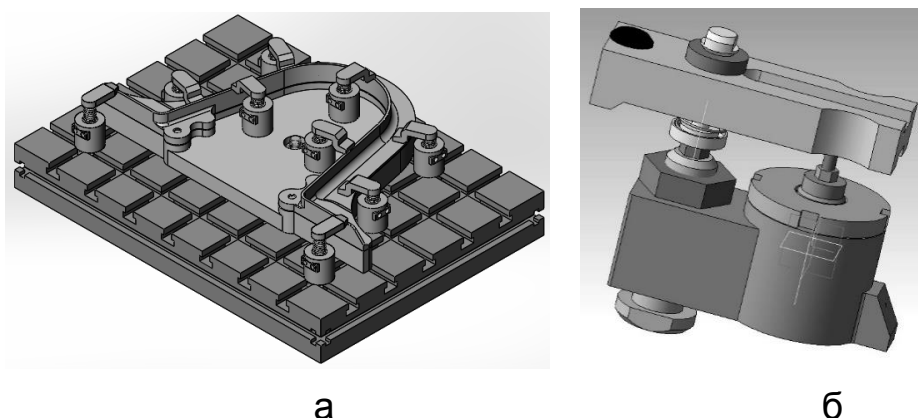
Пример компоновки УСП для фрезерования
